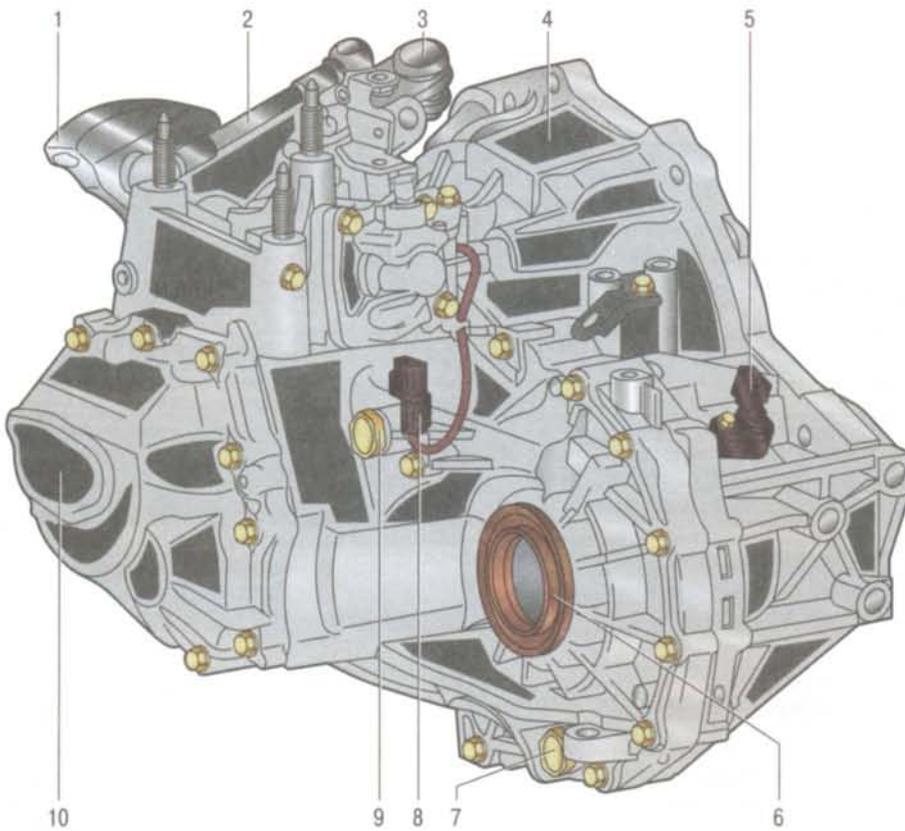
Механическая коробка передач: 1 – груз механизма переключения передач; 2 – рычаг выбора передач; 3 – рычаг переключения передач; 4 – картер сцепления; 5 – датчик скорости; 6 – сальник полуоси; 7 – пробка сливного отверстия; 8 – выключатель света заднего хода; 9 – пробка наливного отверстия; 10 – крышка картера коробки передач
